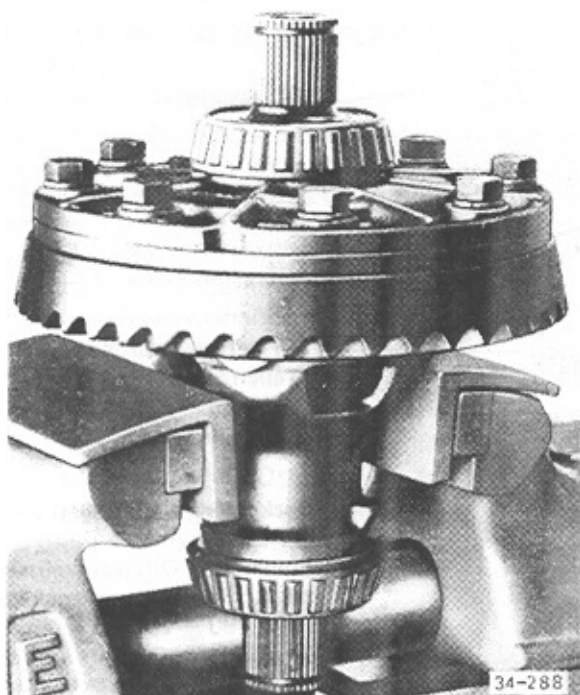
Ausgleichgetriebe in den Schraubstock spannen
